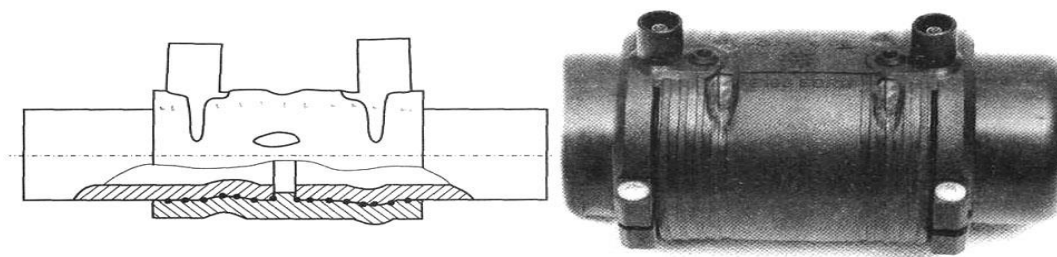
Некачественно выполненное сварное соединение с ЗН (местное расплавление поверхности детали)
